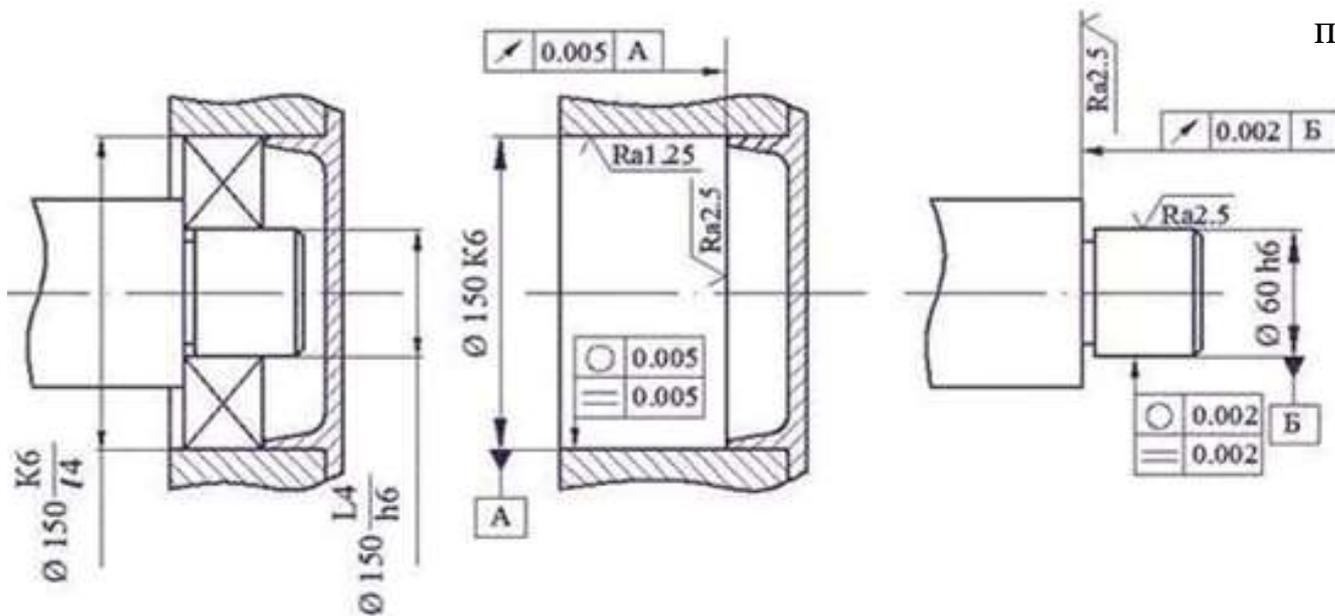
Требования к поверхностям корпуса и вала для установки подшипников качения
